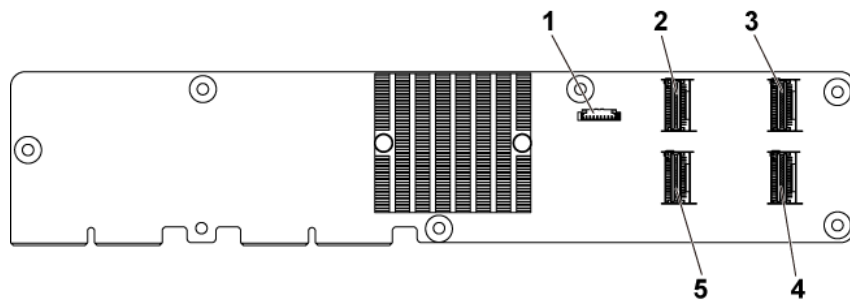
Vue du dessus de la carte d'extenseur de disque dur de 2,5 pouces
